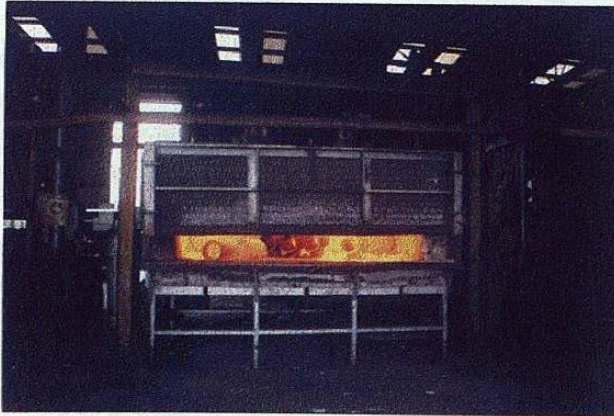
Horno para relevado de esfuerzos de piezas forjadas.
